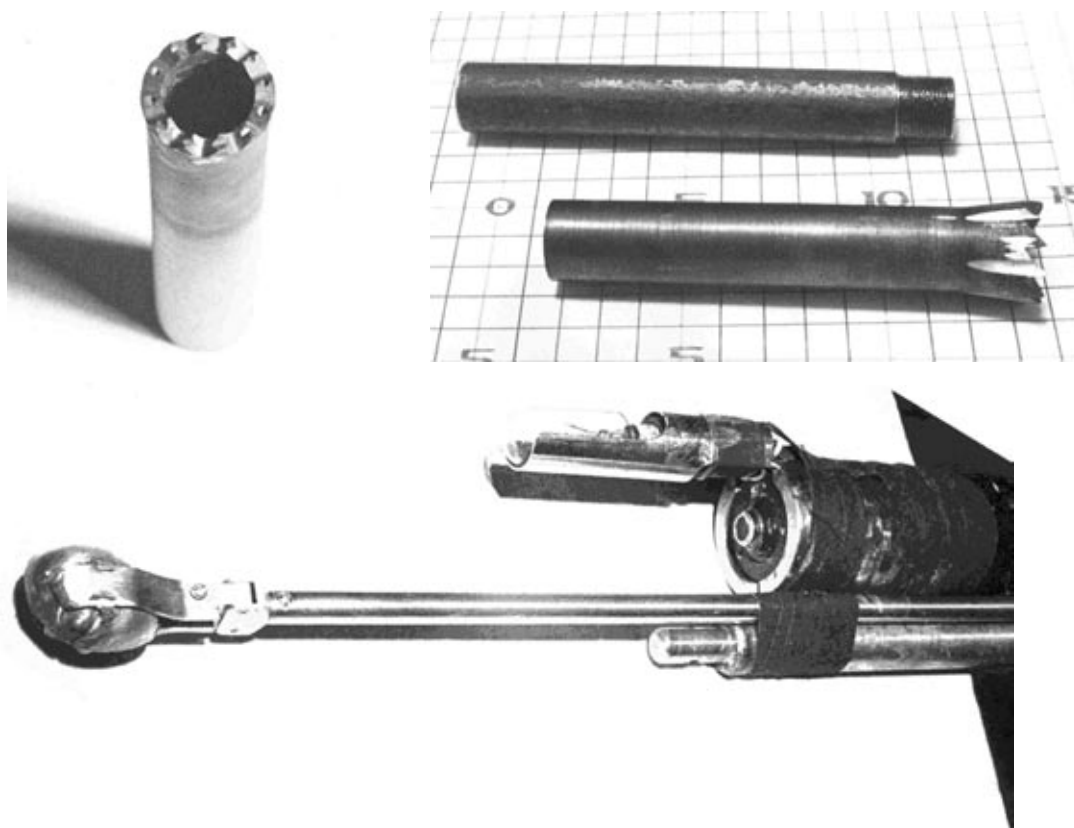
Буровой инструмент (трубчатые фрезы) и специально разработанный комбинированный инструмент (захват + перископ + осветитель) для отбора образцов
